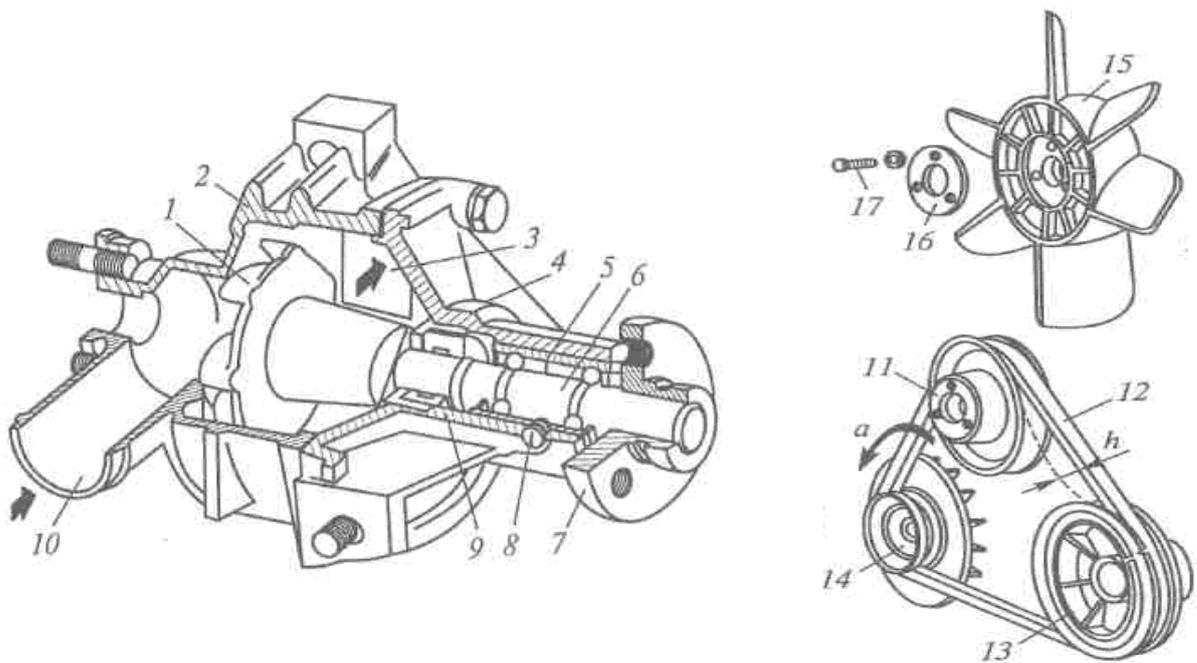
Жидкостный насос и вентилятор двигателя: 1- крыльчатка; 2 – корпус; 3 – окно; 4 – крышка; 5 – подшипник; 6 – вала; 7 – ступица; 8 – винт; 9 – уплотнительной устройство; 10 – патрубков; 11,13,14 – шкивы; 12 – ремень; 15 – вентилятор; 16 – накладка; 17 – болт.
